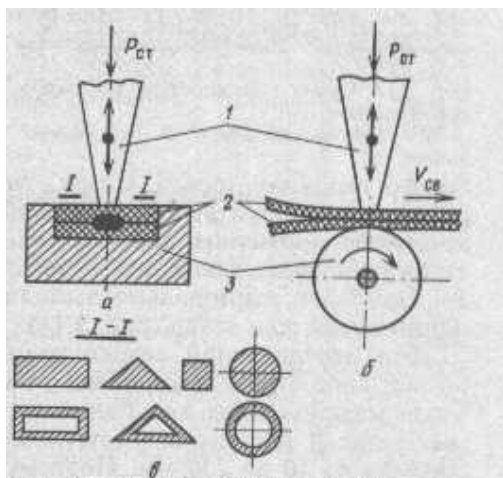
Схема контактной ультразвуковой сварки: а – прессируемая; б – шовная; в – возможные формы рабочего торца волновода; 1 – волновод; 2 – свариваемые детали; 3 – опора
